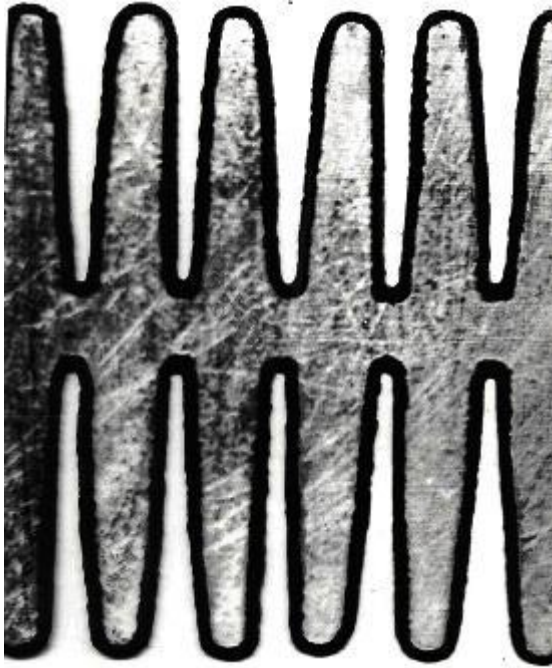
Lamellenstruktur einer formierten Großoberflächenplatte [3]. Die Abb. zeigt eine ältere Version mit unterbrochener Lamellenstruktur.
